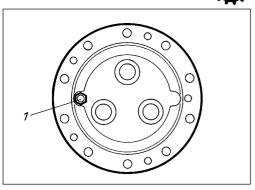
Положение планетарного мехнизма при заливке масла 1. Заглушка
